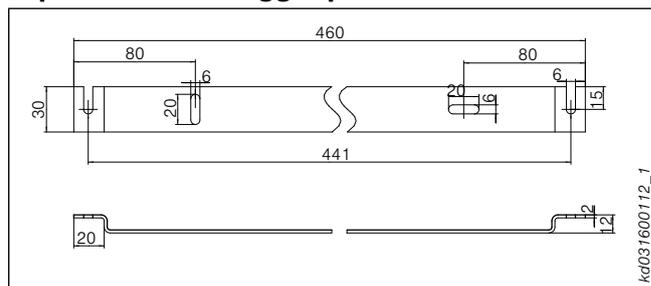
Squadra di montaggio per montaggio esterno del pannello solare
